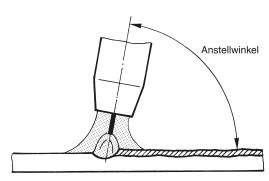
Anstellwinkel des Schweißbrenners
